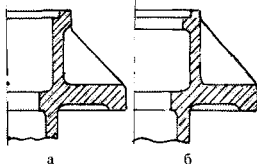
Конструкция литой детали с фланцем: а — наружным; б — внутренним
